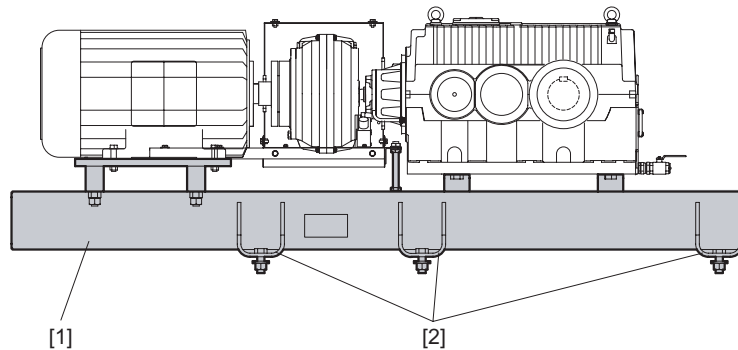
Индустриальный редуктор М.. на фундаментной раме с креплением на лапах 53358АХХ
